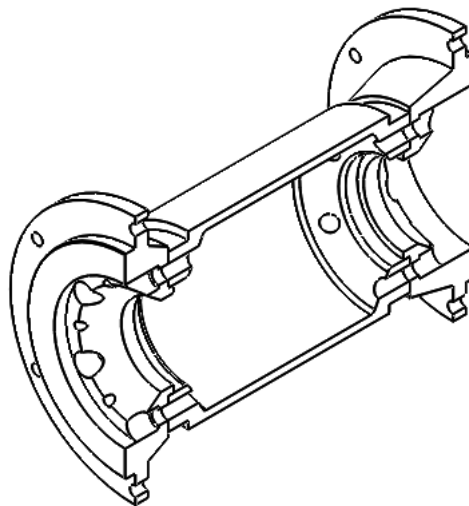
Montagem das flanges no suporte das flanges, vista com corte pelo plano do centro
